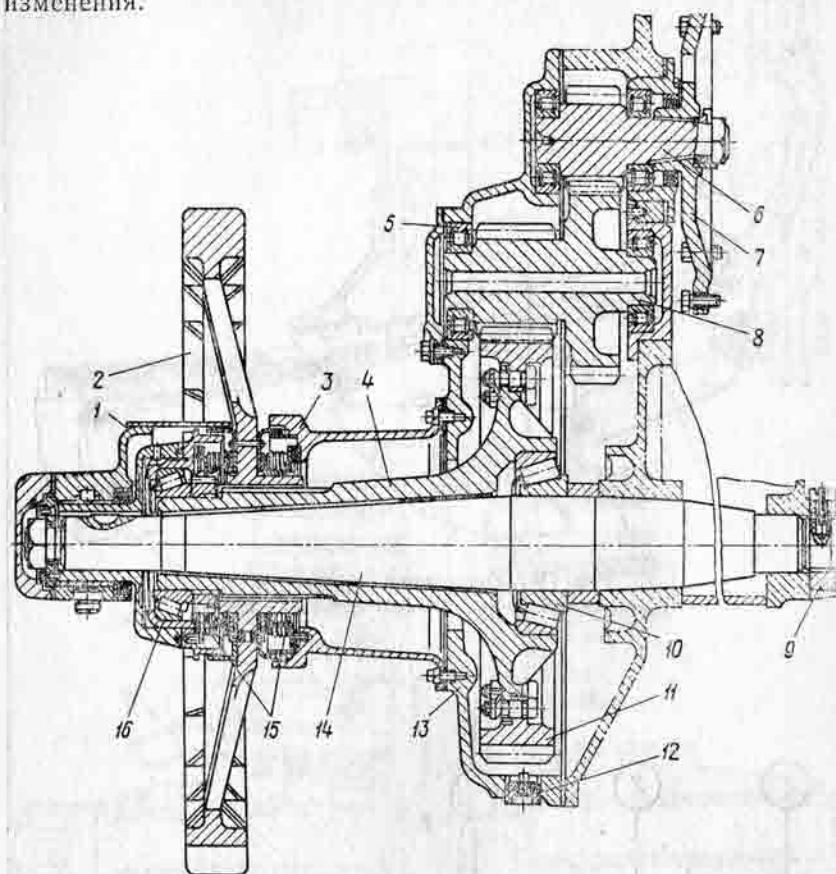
Бортовой редуктор трактора Т-100МБ:
